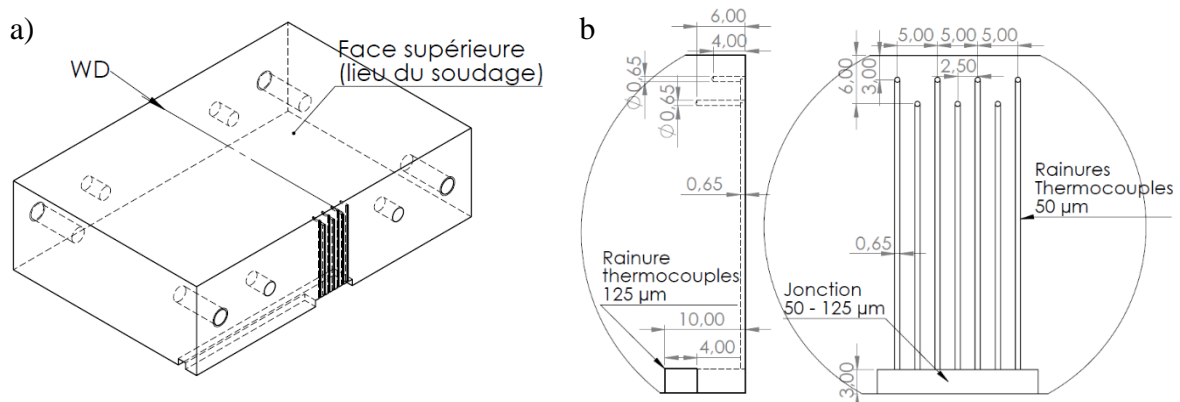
a) usinage d'une portion de l'enclume, b) vue détaillée de l'usinage destiné au passage des thermocouples
